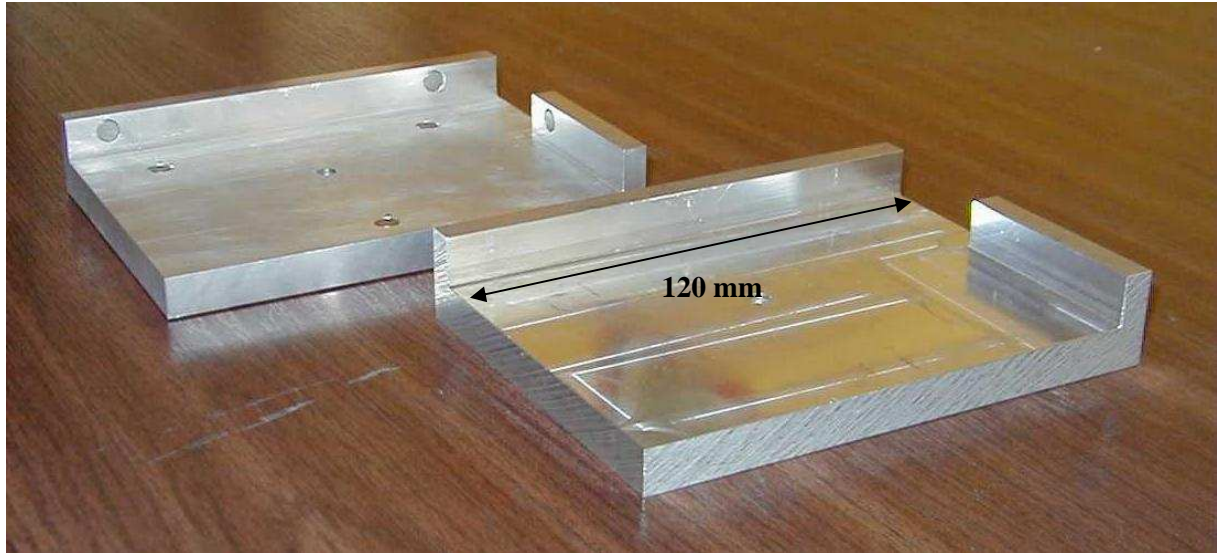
au premier plan, la plate-forme standard en aluminium et derrière le prototype avec inserts en acier.
